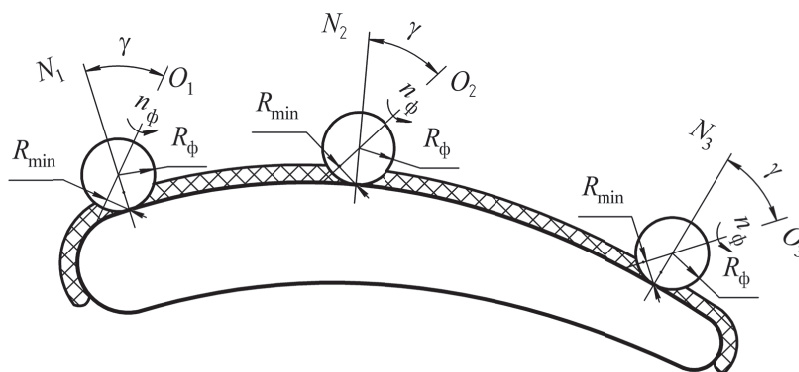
Схема контакта сферической рабочей поверхности фрезы и обрабатываемой поверхности:
